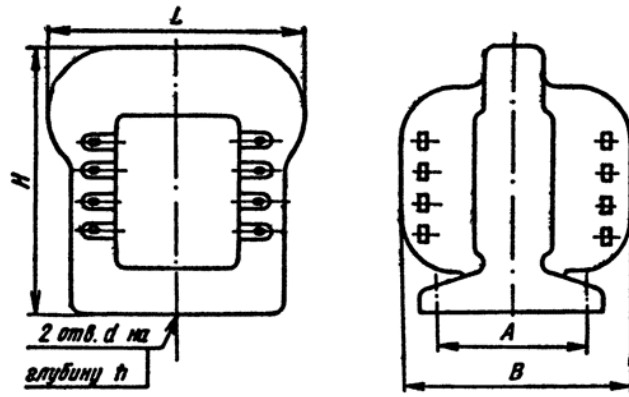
Конструкция броневых трансформаторов типа ТПП с двумя резьбовыми отверстиями для крепления, исполнение В
